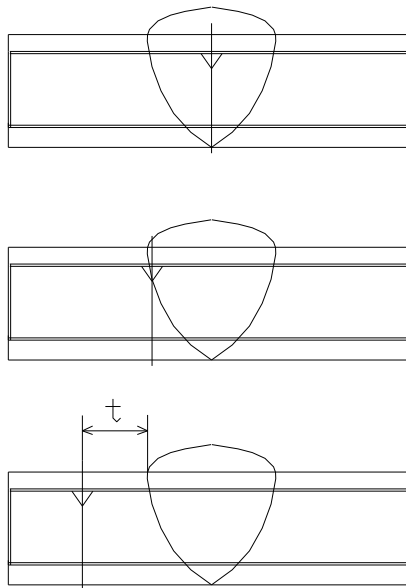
Места вырезки образцов для испытаний на ударный изгиб
